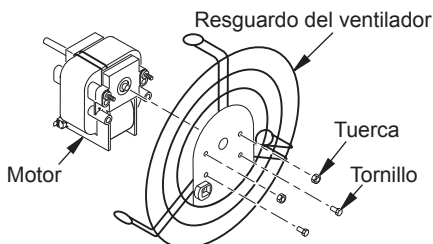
Desmontaje y montaje del resguardo del ventilador en el motor
